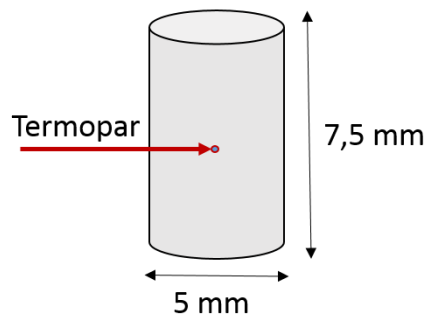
Corpo de prova com região de soldagem dos termopares em destaque.
